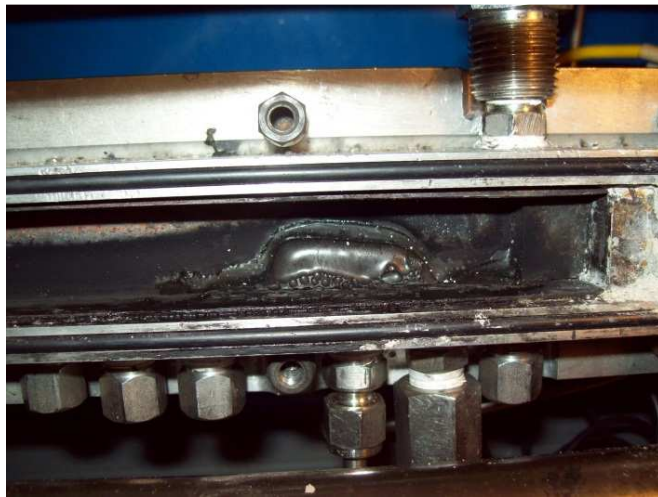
Metamorfosi geometrica del provino in camera di combustione con accessi per termocoppie e accesso per accenditore.
